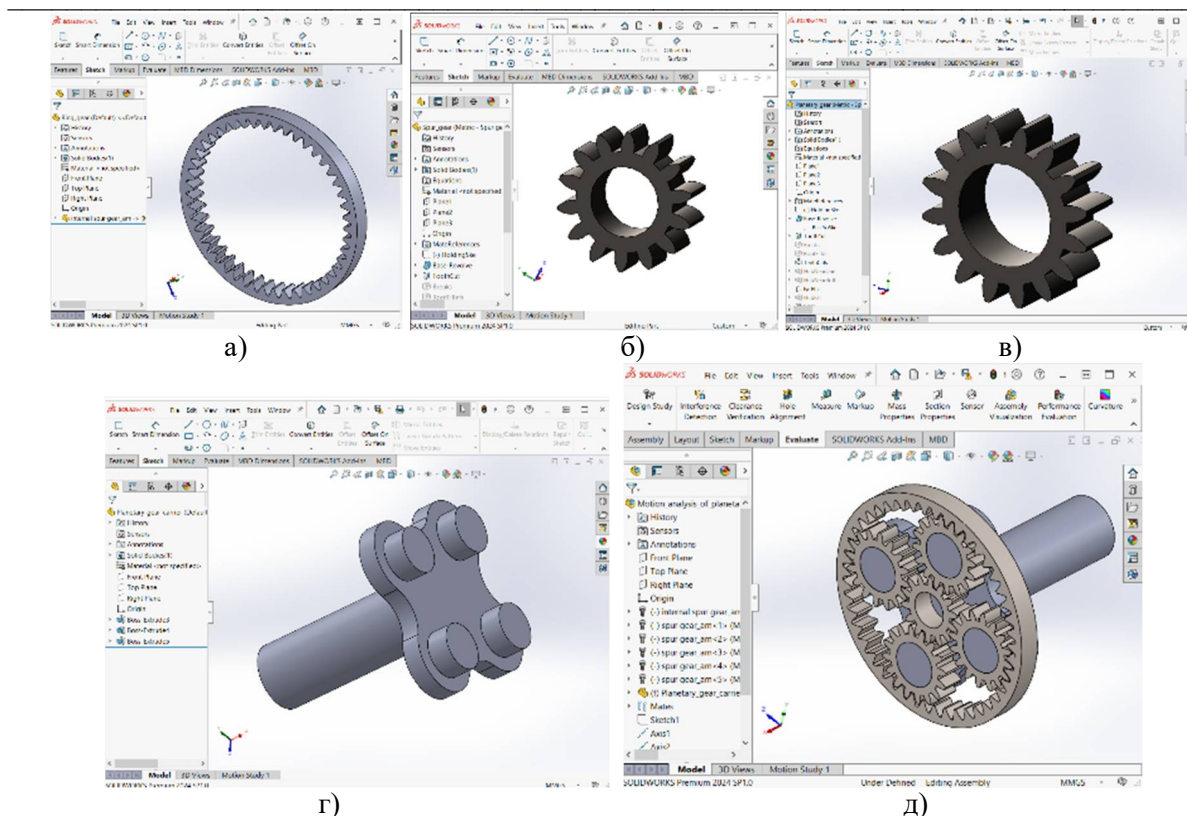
Загальний вигляд деталей планетарного редуктора: а) – вінцева (коронна) шестерня, б) – сонячна (центральна) шестерня, в) – планетарна шестерня, г) – водило, д) - збірка редуктора
